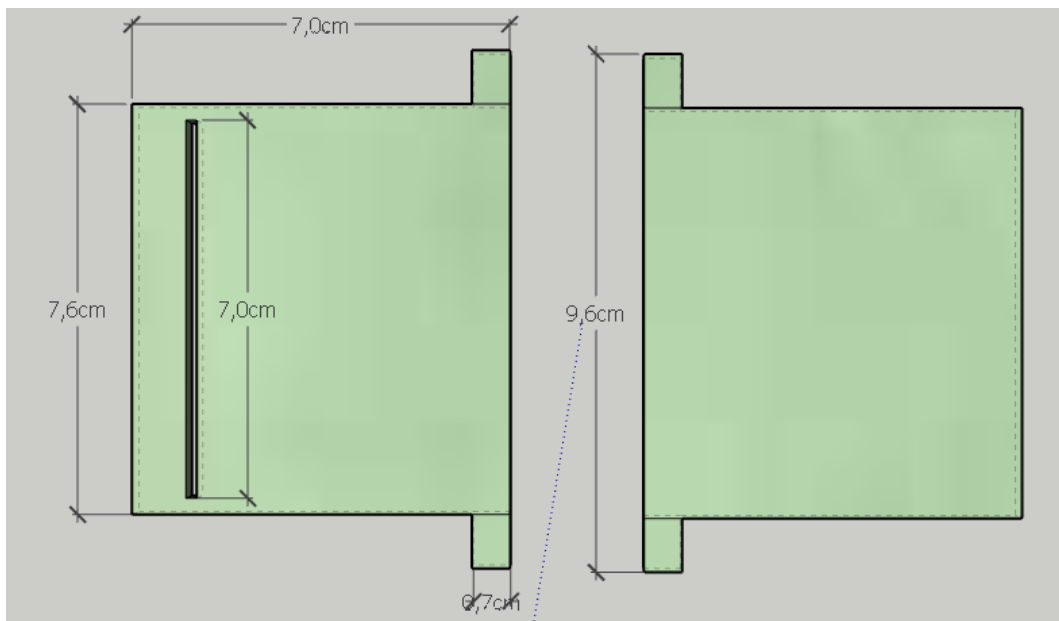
Cubierta superior dividida diseñada en SketchUp Pro 2018.
